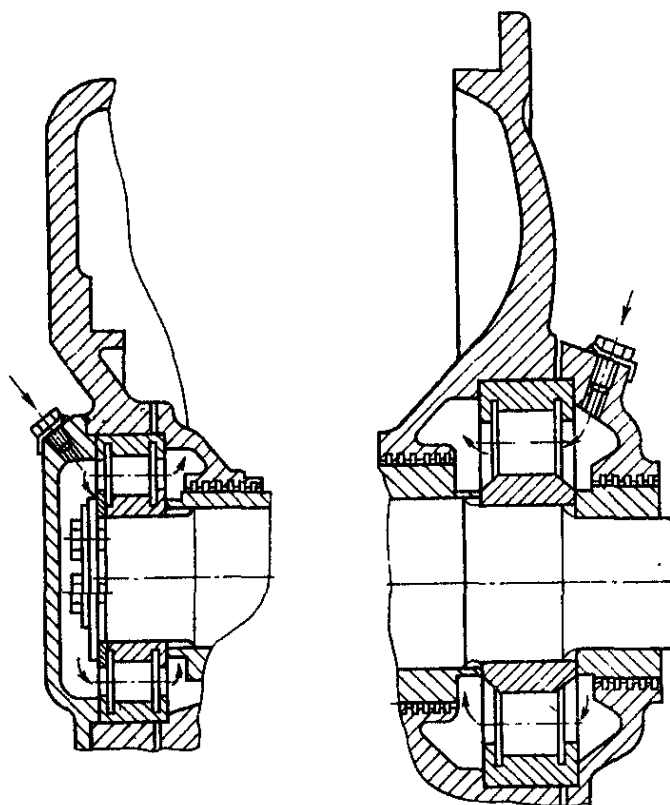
Узлы якорных подшипников мотор-компрессора НБ-431А
